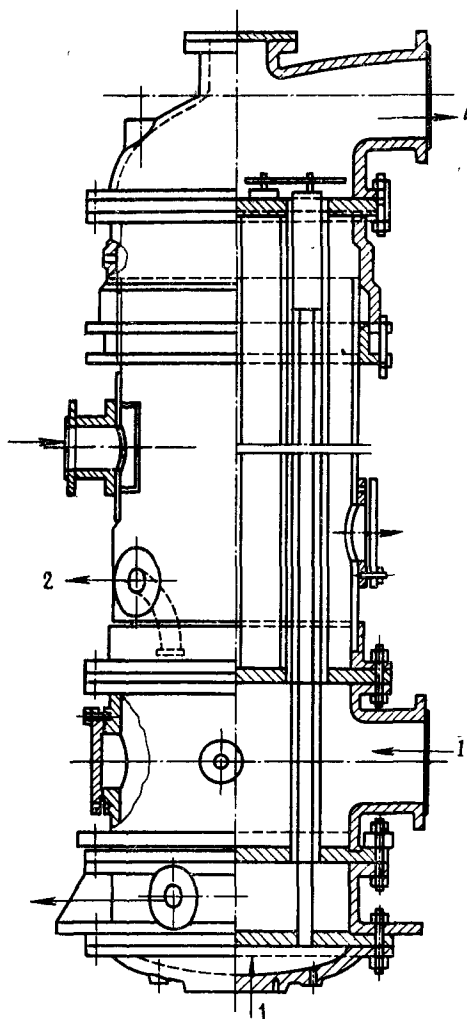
Устройство трубчатого подогревателя типа Бробека:
